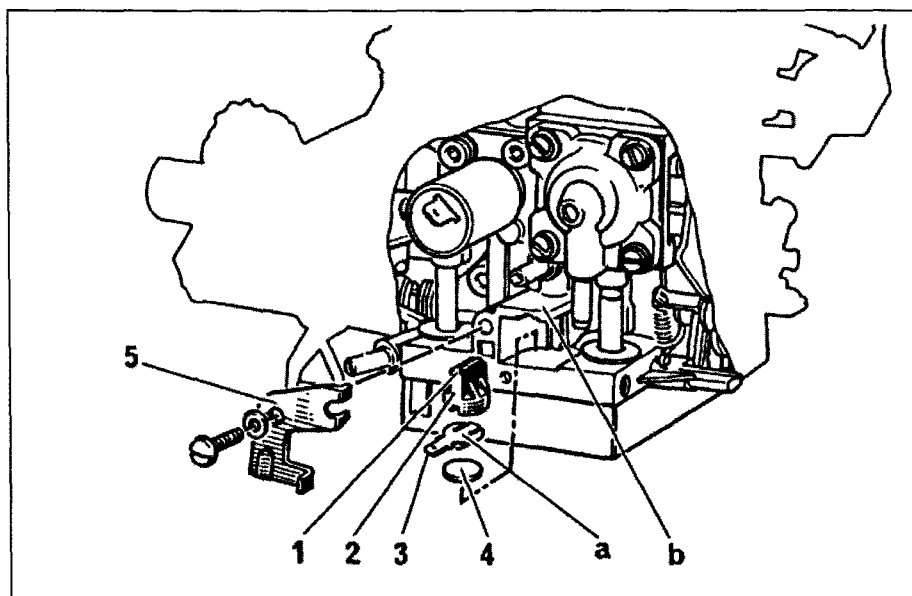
Установка обогревателей корпуса дроссельных заслонок
